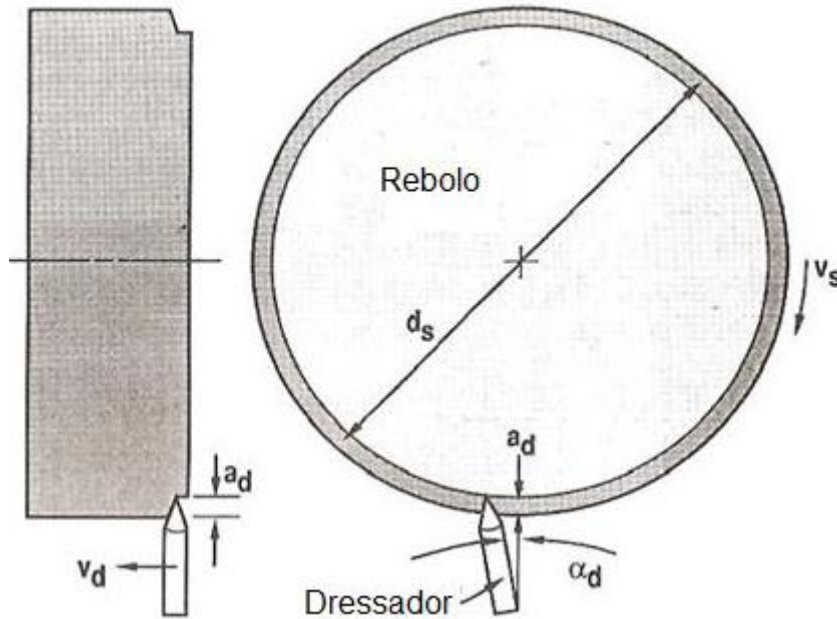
Dressagem de um rebolo por meio de um dressador de ponta única (MALKIN, 2008 - adaptado).
